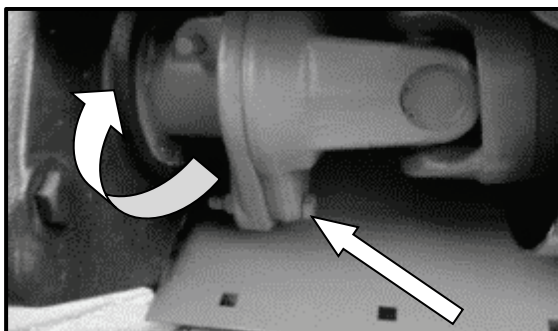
Vista en detalle del tornillo de cizallamiento a la izquierda
